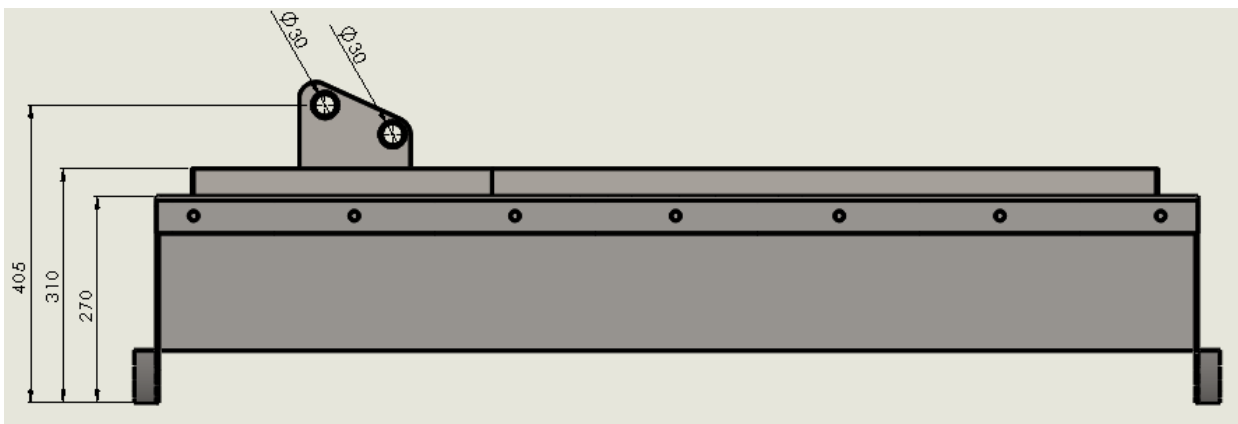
Vista lateral del chasis soporte del rotor de corte.
